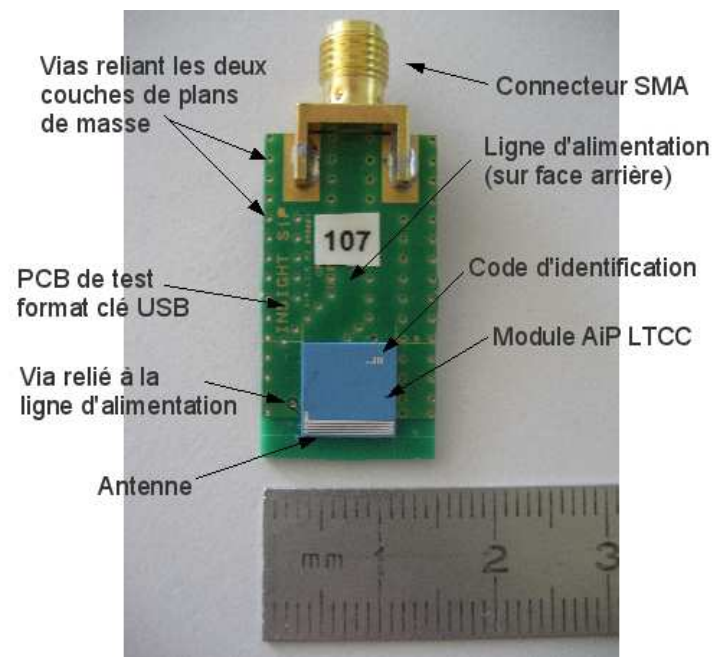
Photographie d'un prototype soudé sur un PCB de type clé USB
